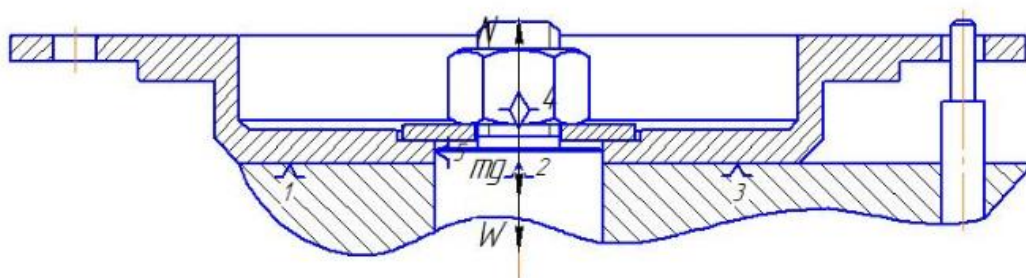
Принципиальная схема зажима заготовки в приспособлении с указанием мест приложения силы зажима.
